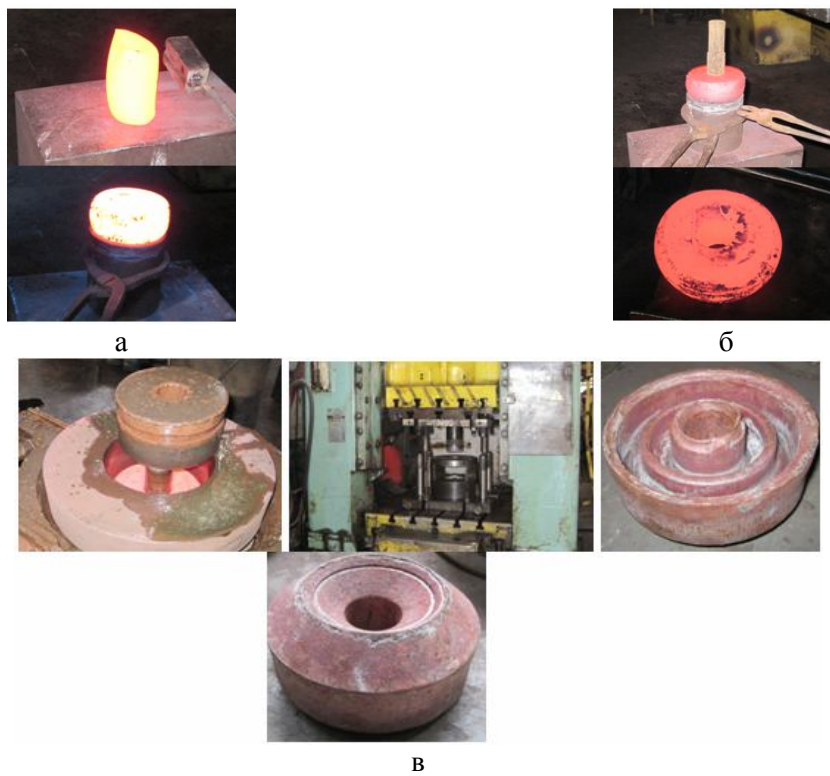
Промышленное внедрение штамповки «Головки кислородной фурмы»: а – заготовка и подготовительная осадка; б – прошивка и прошитая заготовка; в – предварительная и окончательная штамповка (фотографии оборудования и поковок)
